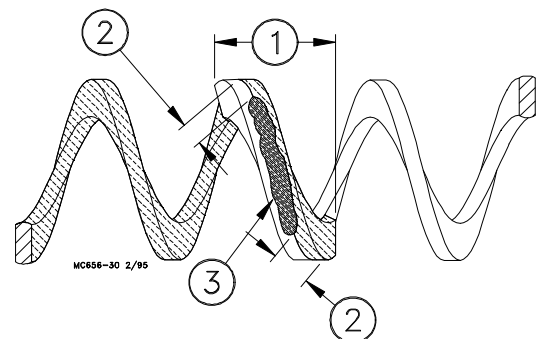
Soldadura en bronce del sinfín (vista lateral)
